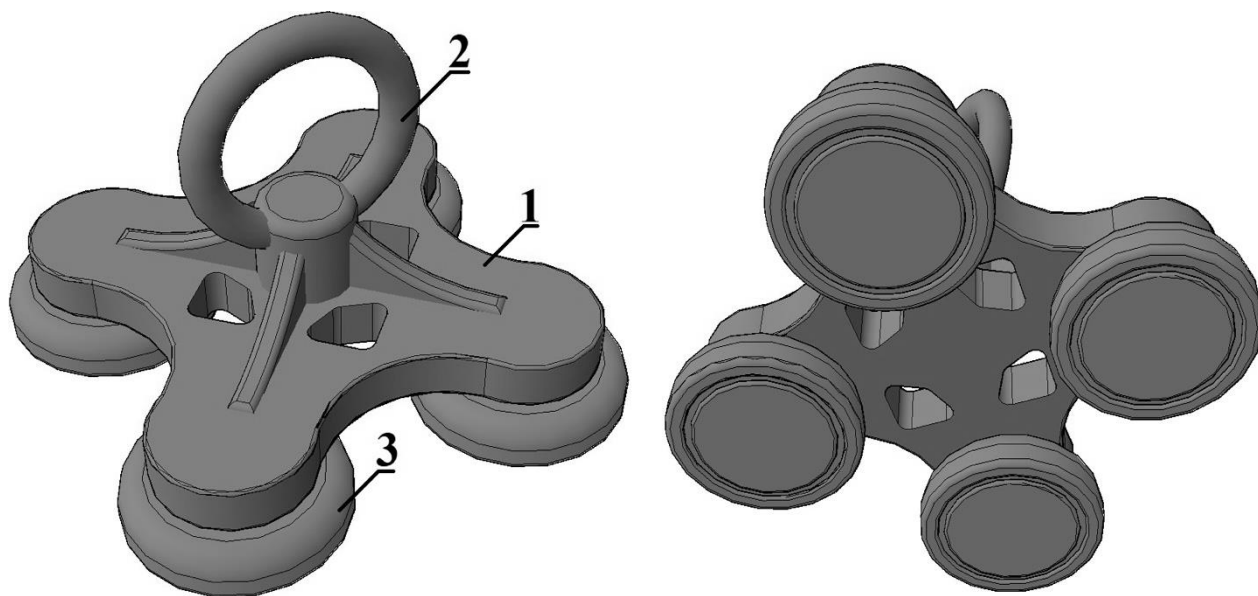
3D модель магнитного устройства: 1 – корпус из немагнитного материала, 2 – рым-гайка М6, 3 - магнитное крепление С36 с винтом М6
